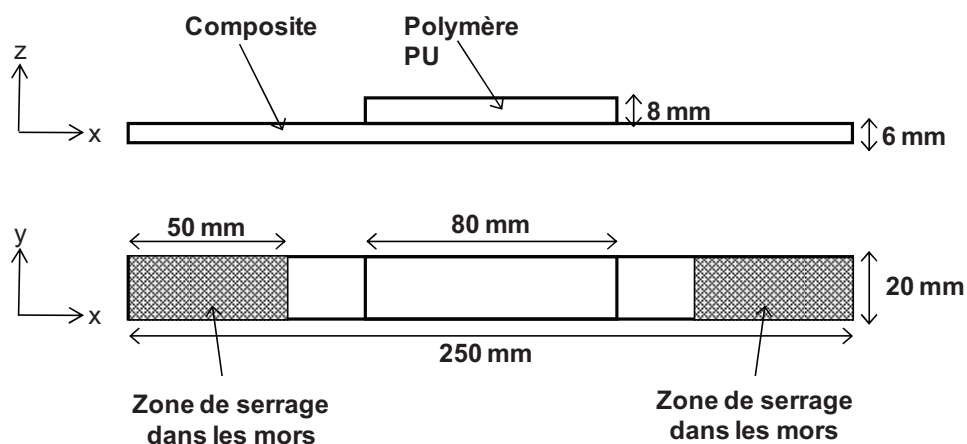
Géométrie des éprouvettes testées en fatigue thermomécanique.
